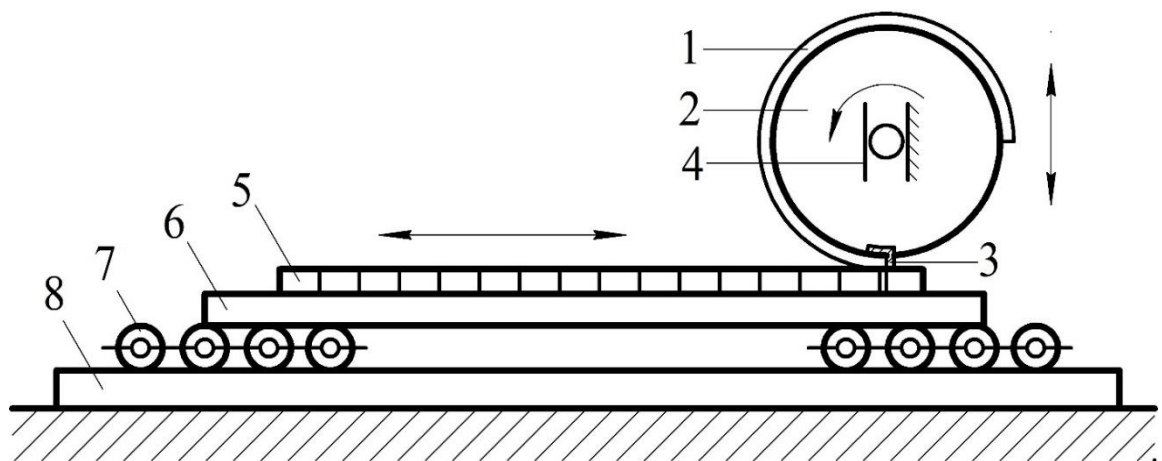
Графічна схема стоп-циліндрового висікального пресу 1 – заготовка палітурного матеріалу; 2 – металевий циліндр; 3 – затискачі; 4 – куліса; 5 – висікальна форма; 6 – талер; 7 – рольганг; 8 – нерухома станина
